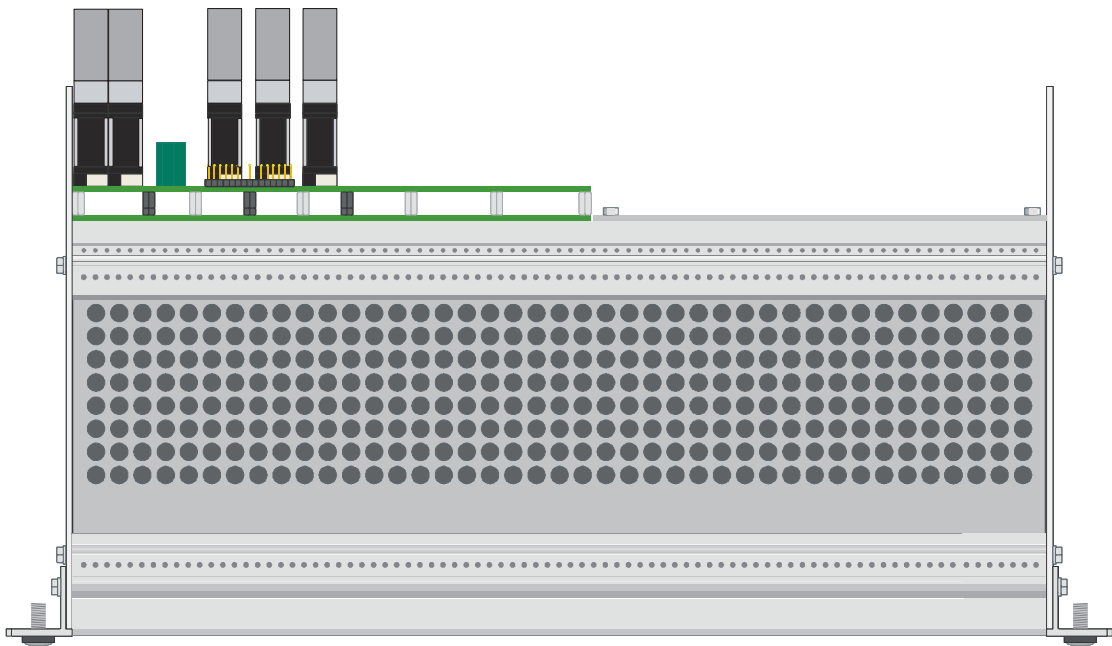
Draufsicht des Baugruppenträgers Type BGT04 mit Beschriftungsleiste und einer ABP
